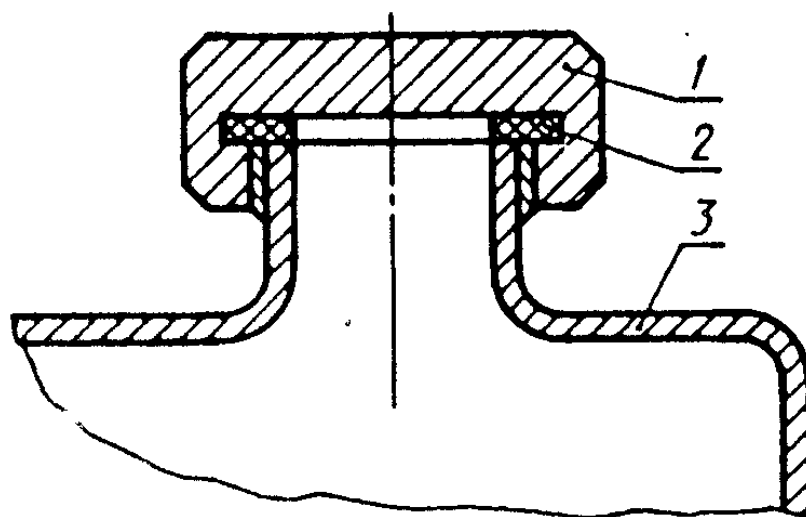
Обозначение сборочных единиц на операции сборки-разборки
